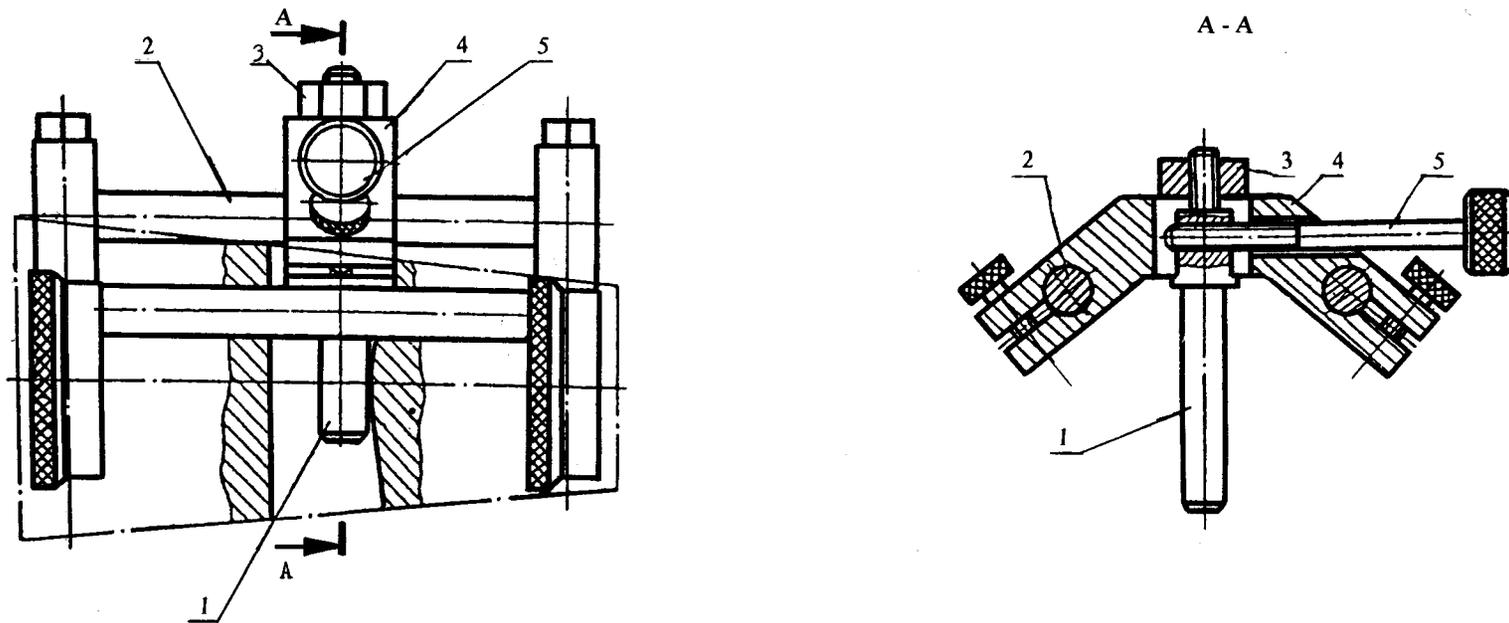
Приспособление для измерения конусов инструментальных оправок:
